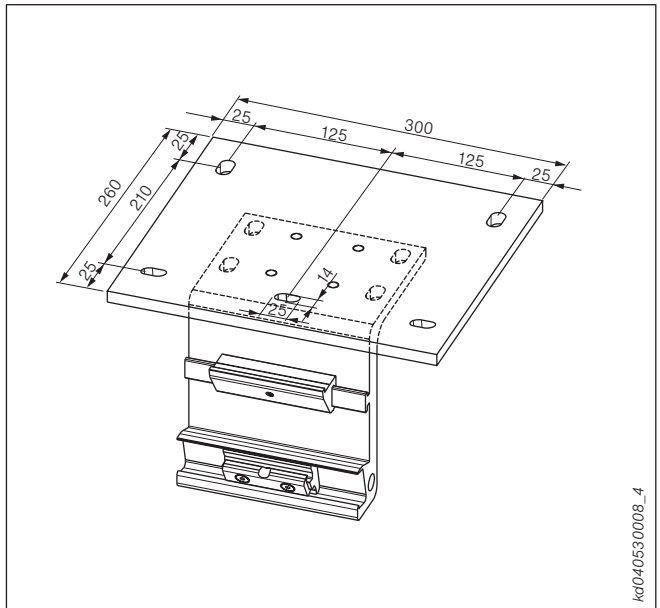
Consola tipo E – Fijación en el techo fija, salida 400 cm
